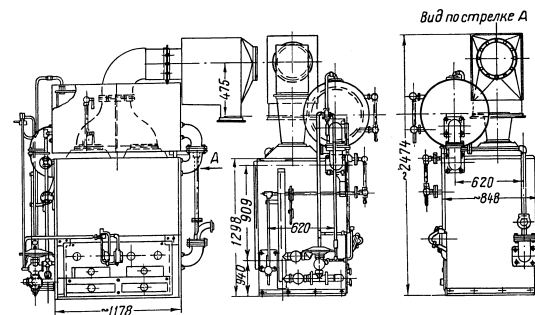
Габаритные размеры парового котла „ЛУЧ“ с поверхностью нагрева 14,72 м²
